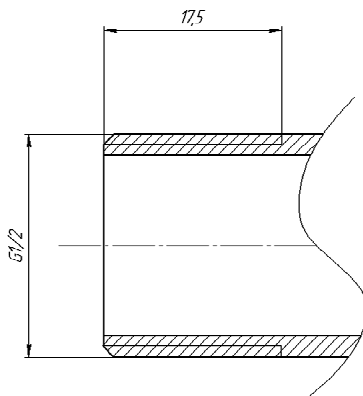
Присоединительные размеры патрубка рубашки обогрева
